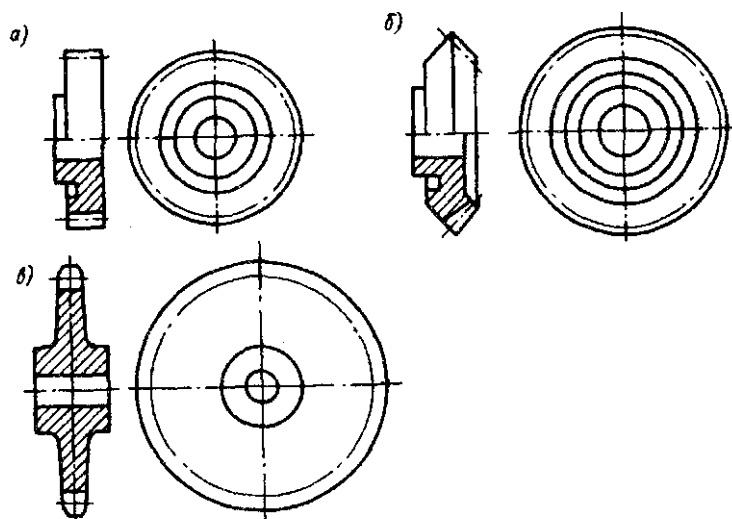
Изображение зубчатых колес: а — цилиндрического; б — конического; в — звездочки цепной передачи
